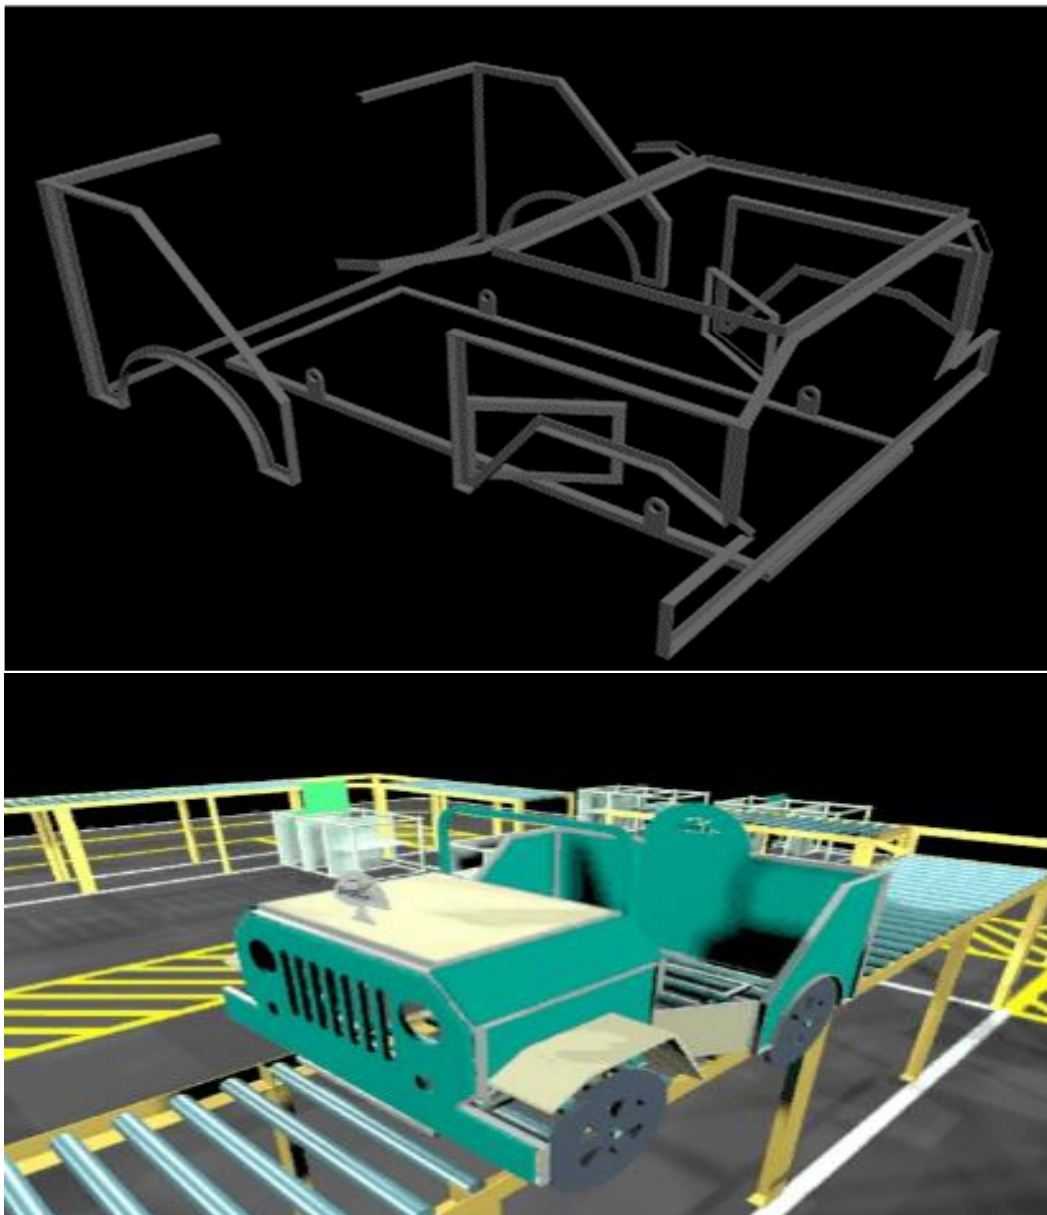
Sketch de un vehículo tipo Jeep construido con perfiles angulares de acero y planchas de madera.
